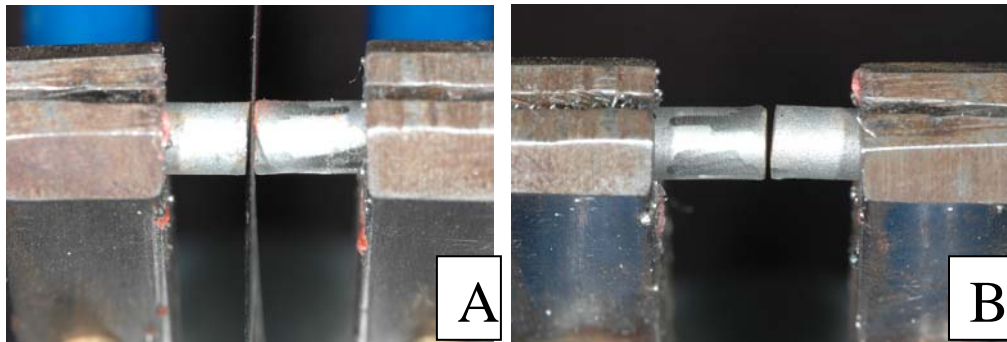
Matriz com a lâmina metálica de 0,1mm posicionada para determinar o espaço da solda (A), espaço de 0,1 mm para soldagem (B)
